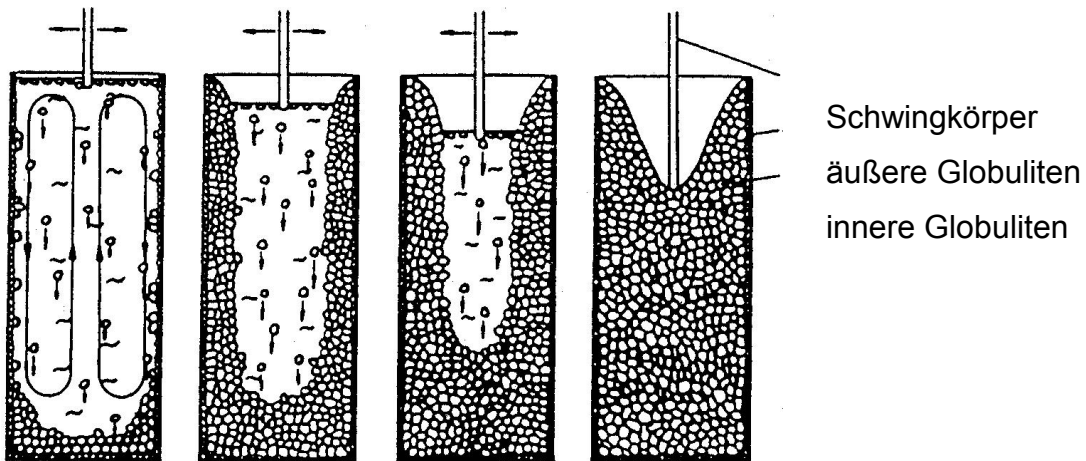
Entstehung des Gussgefüges durch mechanische Manipulation der Oberfläche [22]
